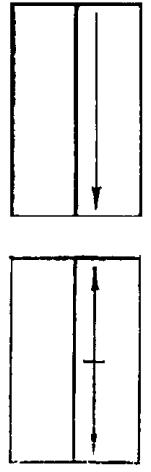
Последовательность наложения наплавки при сварке:
